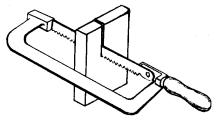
Forma de utilización 3.1.2.1 Serrucho mecánico
